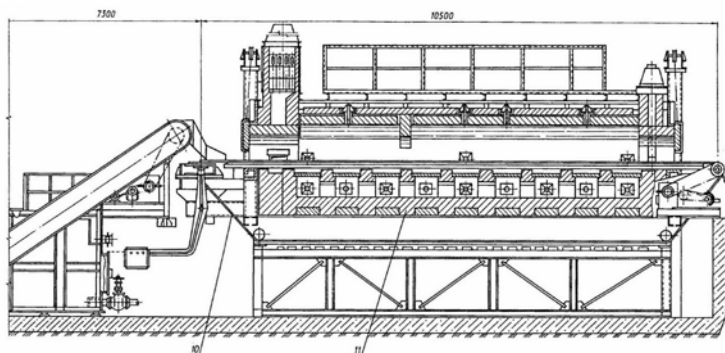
Конструкция газопламенной печи конвейерного типа [1]
